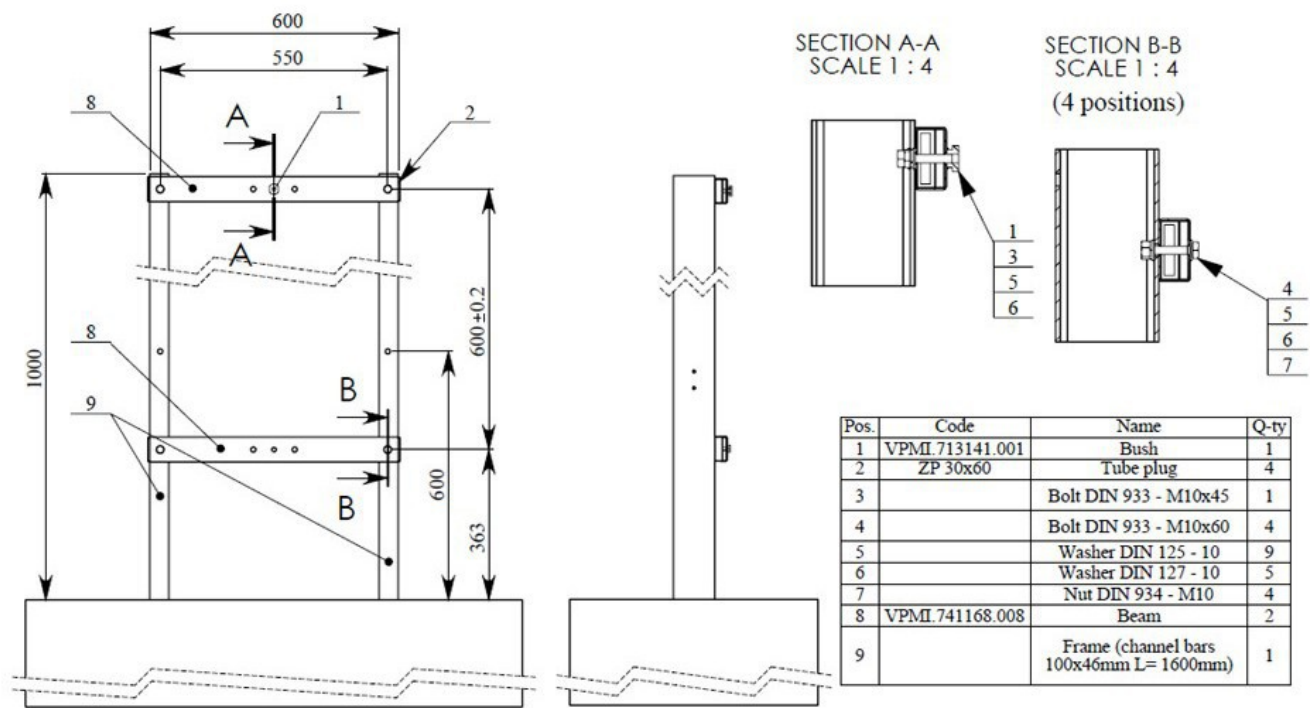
Montaje de vigas y casquillos en el pilar inferior de PoliGate Light G2
